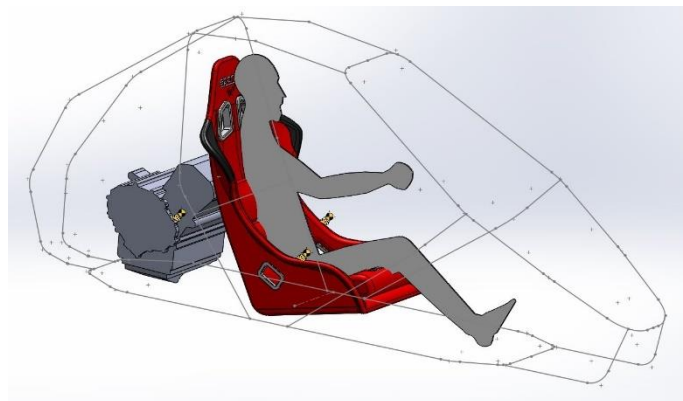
Dimensionado de los elementos principales del chasis
